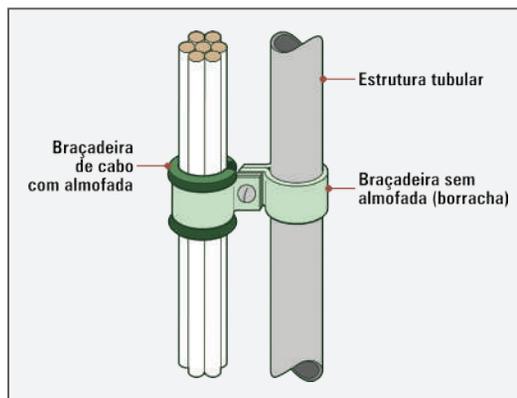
Instalação da braçadeira de cabo na estrutura tubular
